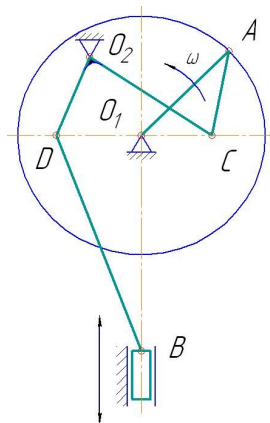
Кінематична схема 6-ти ланок механізму витяжного преса
